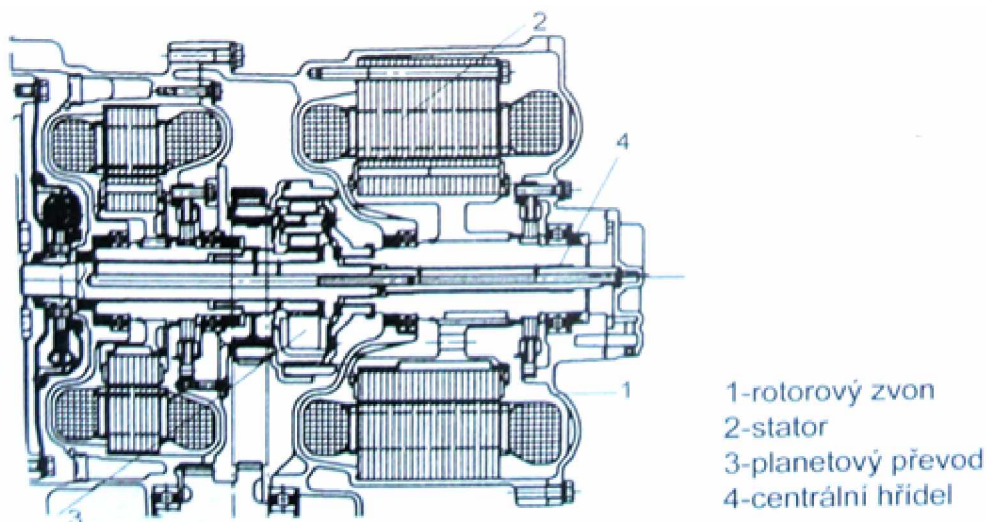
Schéma a řez motorem firmy Magnet-Motor [1]
